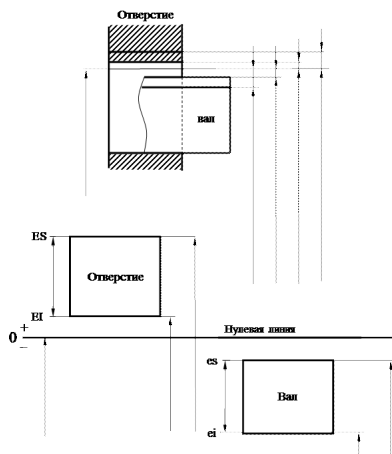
Схемы полей допусков вала и отверстия
